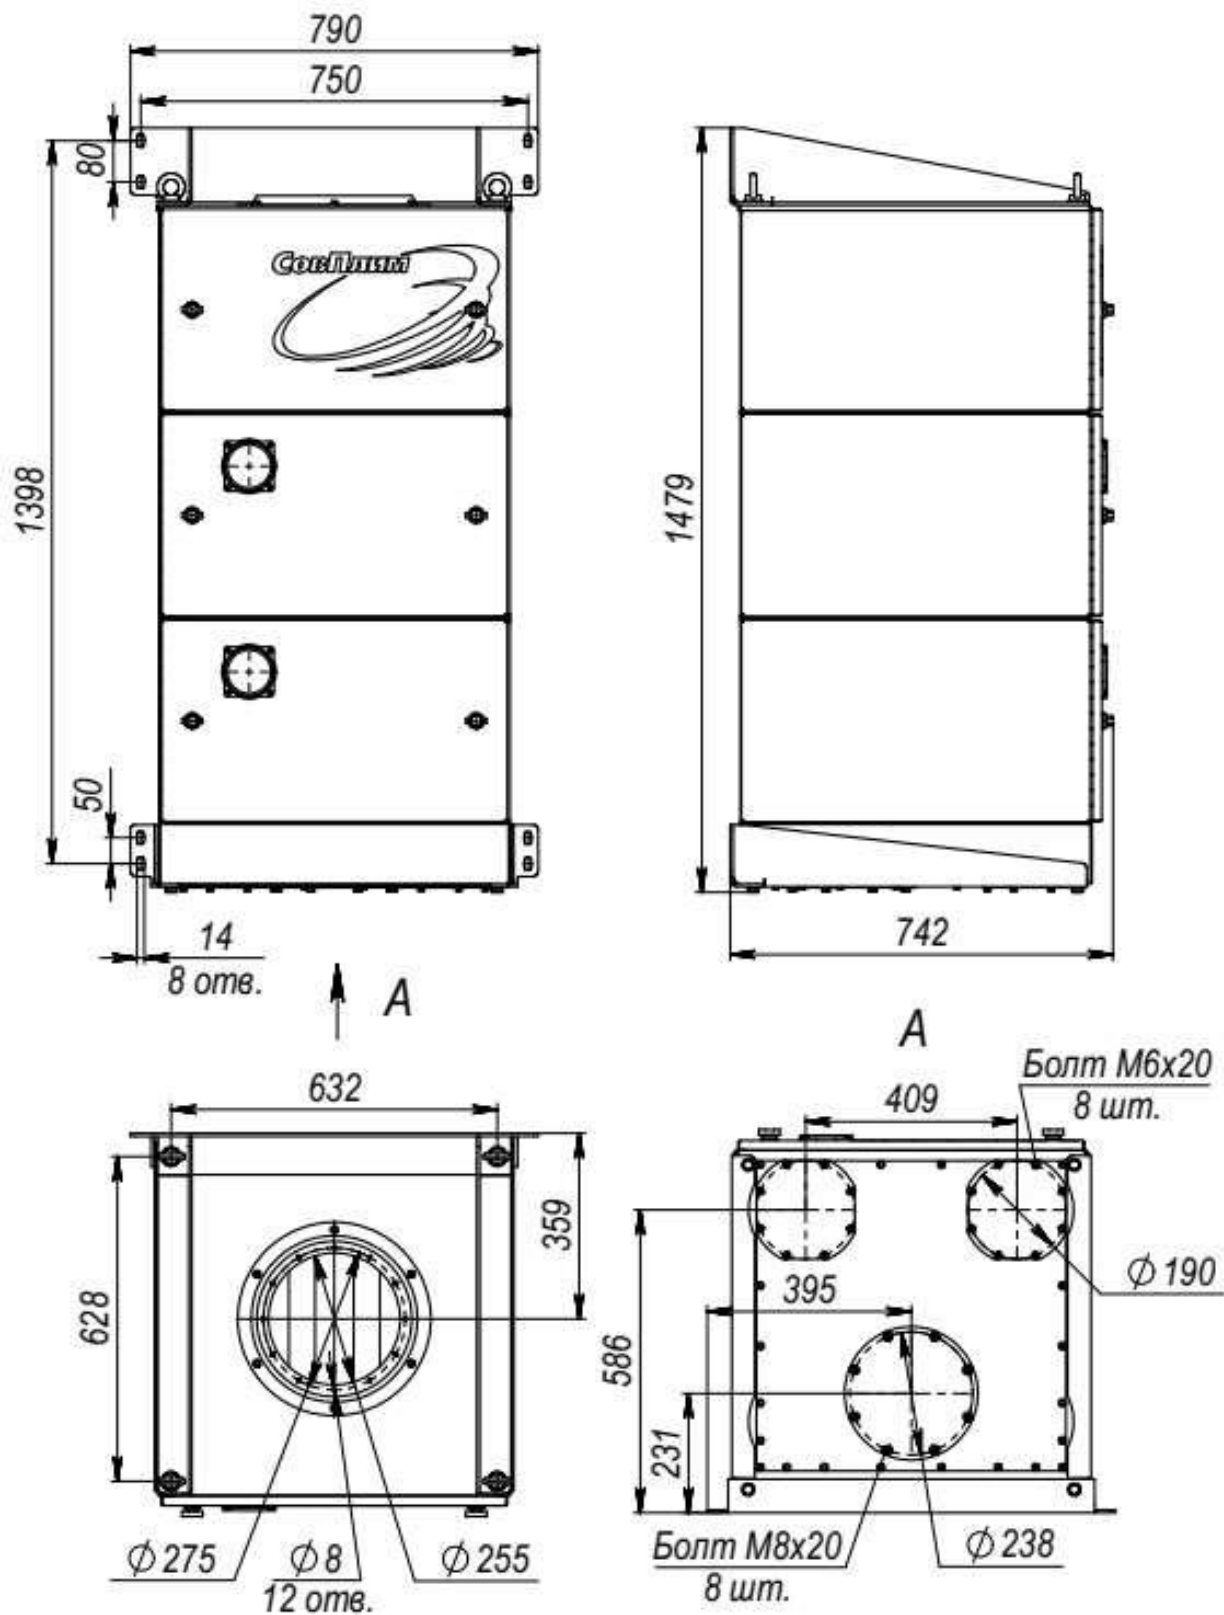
Габаритные размеры фильтра MF-H-42
